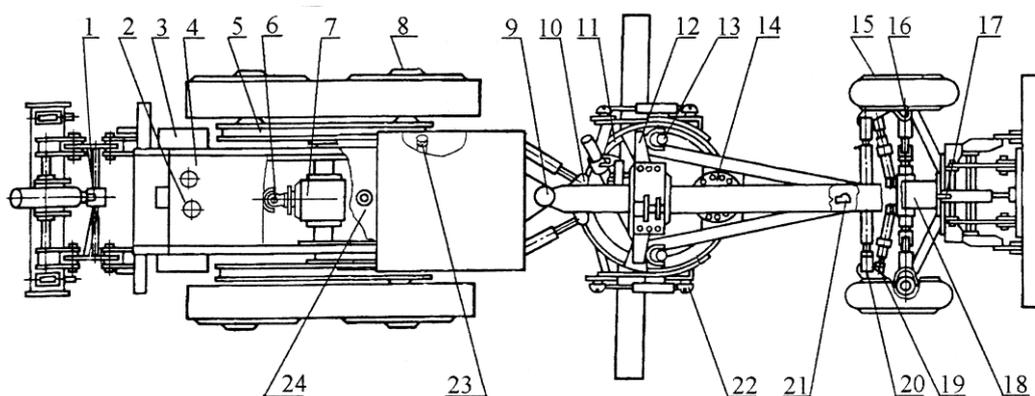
Схема смазки автогрейдера ДЗ-122Б: 1 – шарниры подвески кирковщика (Литол-24); 2 – картер двигателя (Mobil Delvac); 3 – клеммы аккумуляторных батарей (смазка ПВК); 4 – картер гидромеханической коробки передач (Mobiltrans HD); 5, 7, 8 – балансиры и картер главной передачи задней тележки, планетарные колесные редукторы (трансмиссионное масло SAE 90); 6 – шарниры карданного вала (158В); 9 – подшипники шарнира складывания рамы; 10 – шарнирные подшипники гидроцилиндров складывания рамы; 11 – направляющие отвала, зубчатое колесо механизма поворота отвала, зубчатый венец; 12 – подшипники цапфы гидроцилиндров; 13 – подшипники вилок и шаровые цапфы гидроцилиндров (все – Литол-24); 14 – редуктор поворота отвала (ТАп-15В); 15 – ступицы передних колес; 16 – верхние и нижние втулки шатунов передних колес; 17 – шаровые крышки гидроцилиндров и шарниров бульдозерного отвала; 18 – ось шатуна наклона колес, центральные оси переднего моста; 19 – втулки пальцев гидроцилиндров рулевого управления; 20 – сферические пальцы рулевой трапеции; 21 – гнездо шкворня тяговой рамы; 22 – шарнирные подшипники гидроцилиндров изменения угла резания отвала (все – Литол-24); 23 – гидросистема (ВМГЗ); 24 – система охлаждения двигателя (антифриз)
